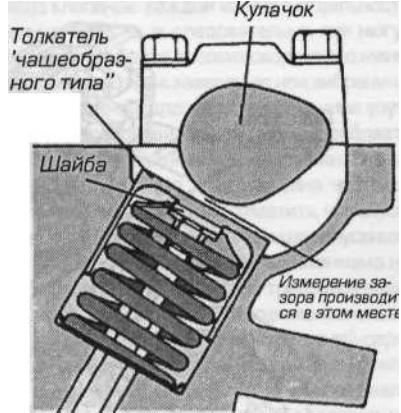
Типичный механизм привода газораспределения типа DOHC в разрезе, показывающем устройство чашеобразных толкателей с регулировочными шайбами снизу
